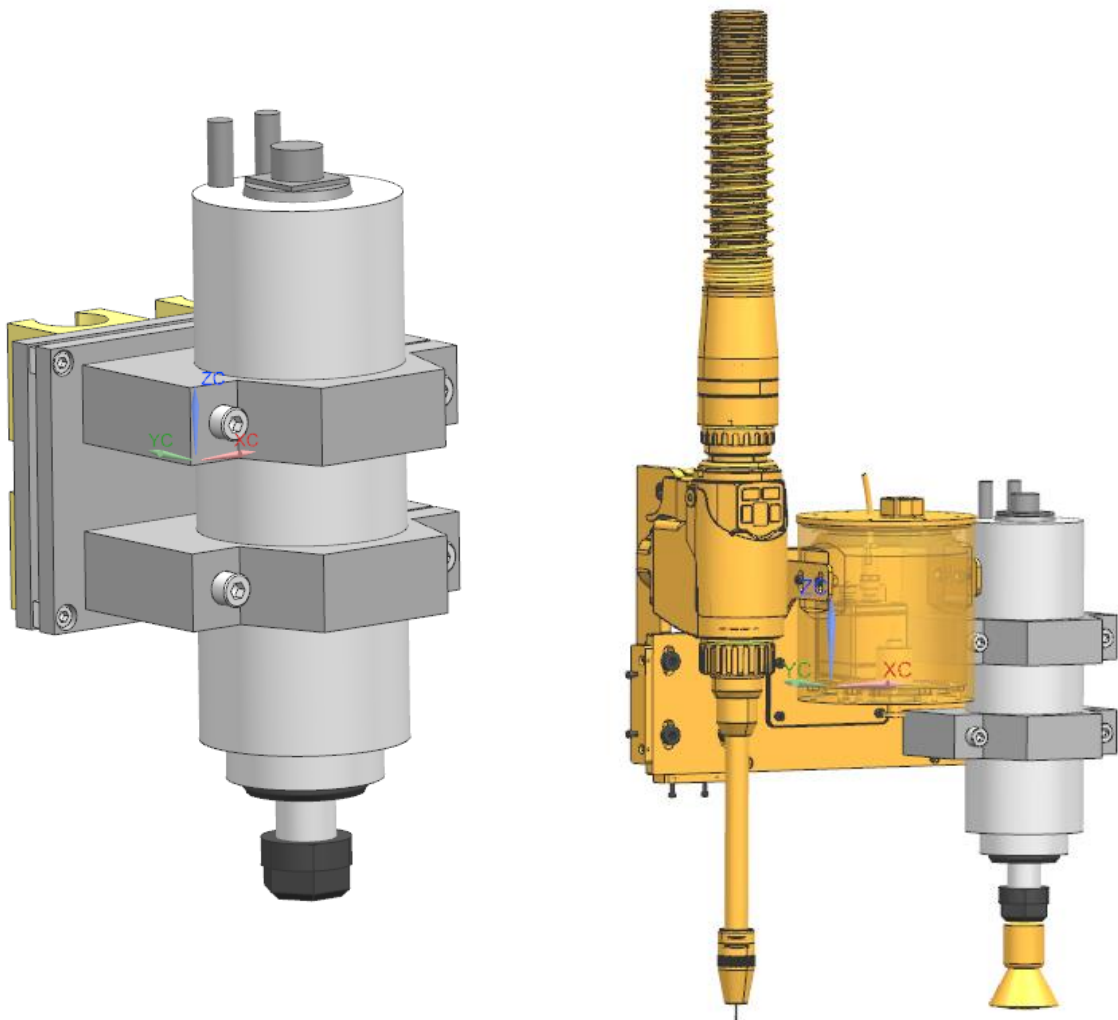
Izomerický pohled na upravenou konstrukci stojanu.
